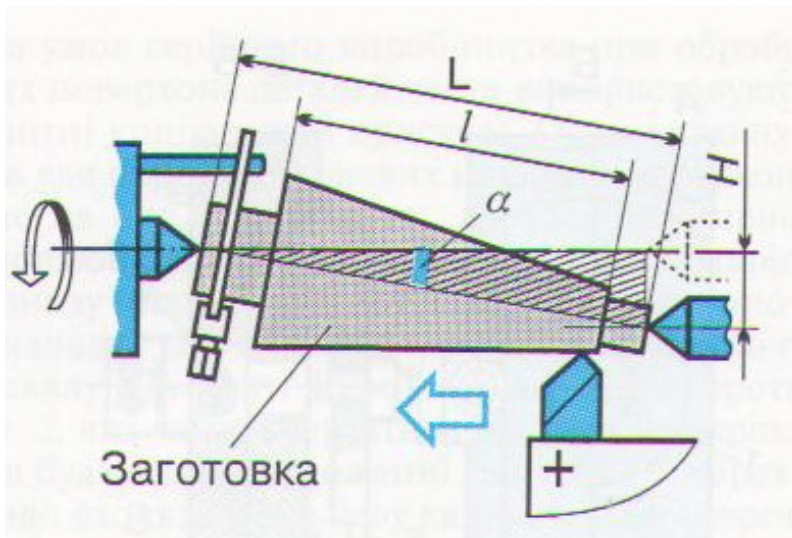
Обробка зовнішньої конічної поверхні способом зміщення корпусу задньої бабки:
